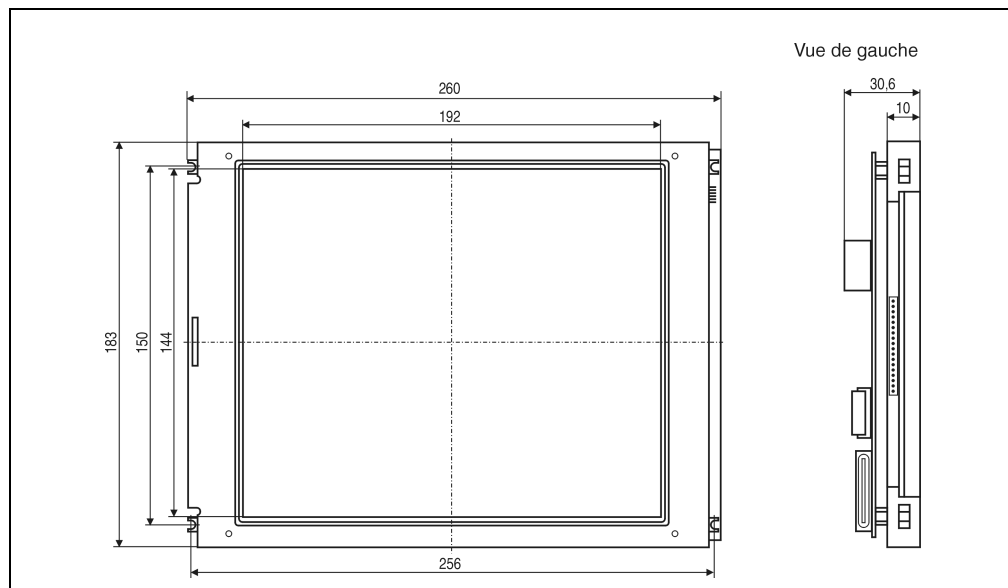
Dimensions du kit écran 5D2000.10 (9,4 pouces)
